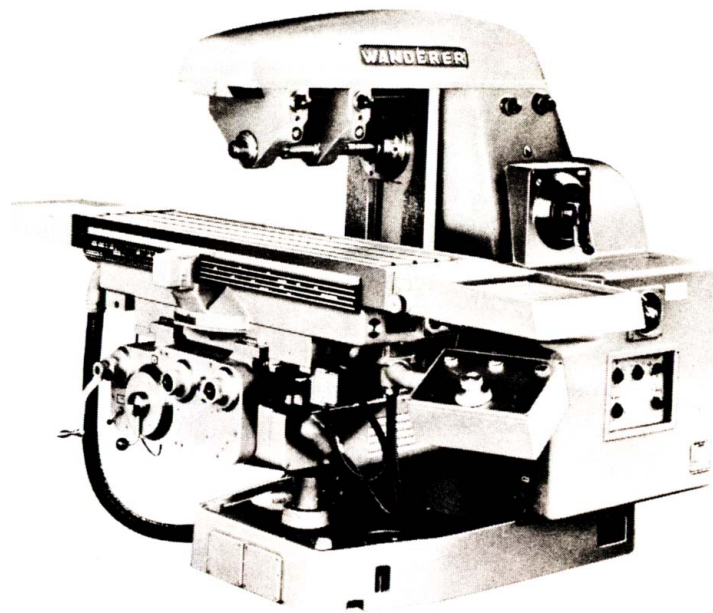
Máquina fresadora universal (con mesa de fresar basculante)
